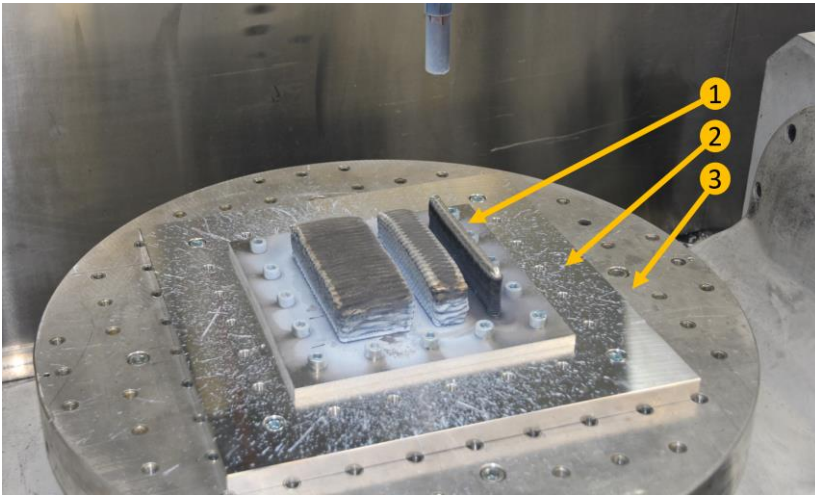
Versuchsaufbau Fräsbearbeitung [1] Substratplatte, [2] Adapterplatte, [3] Maschinentisch
